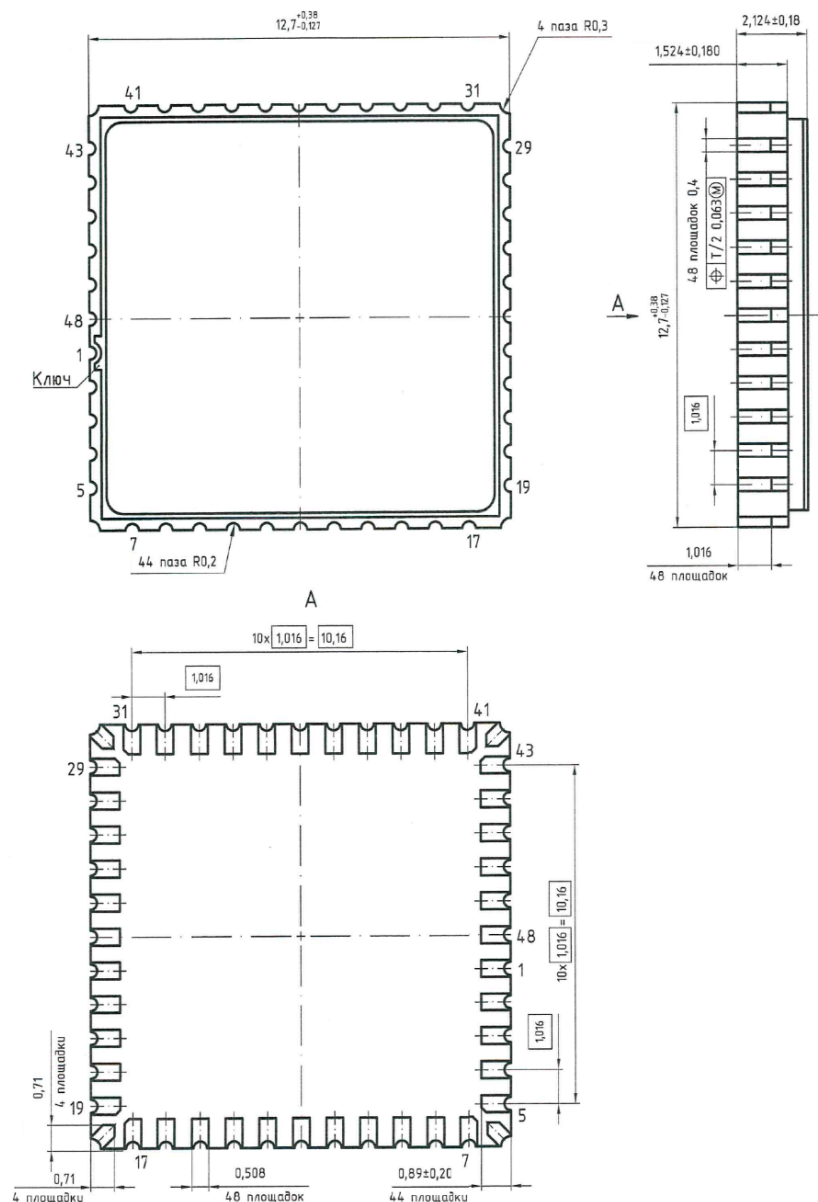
Габаритный чертеж корпуса 5142.48-A (размеры в мм)
